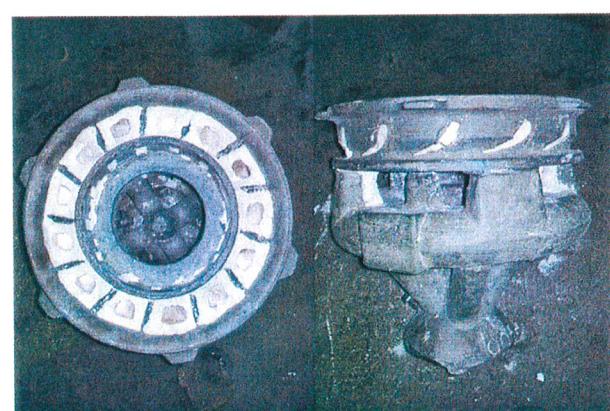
Общий вид отливки после удаления остатков керамической формы
